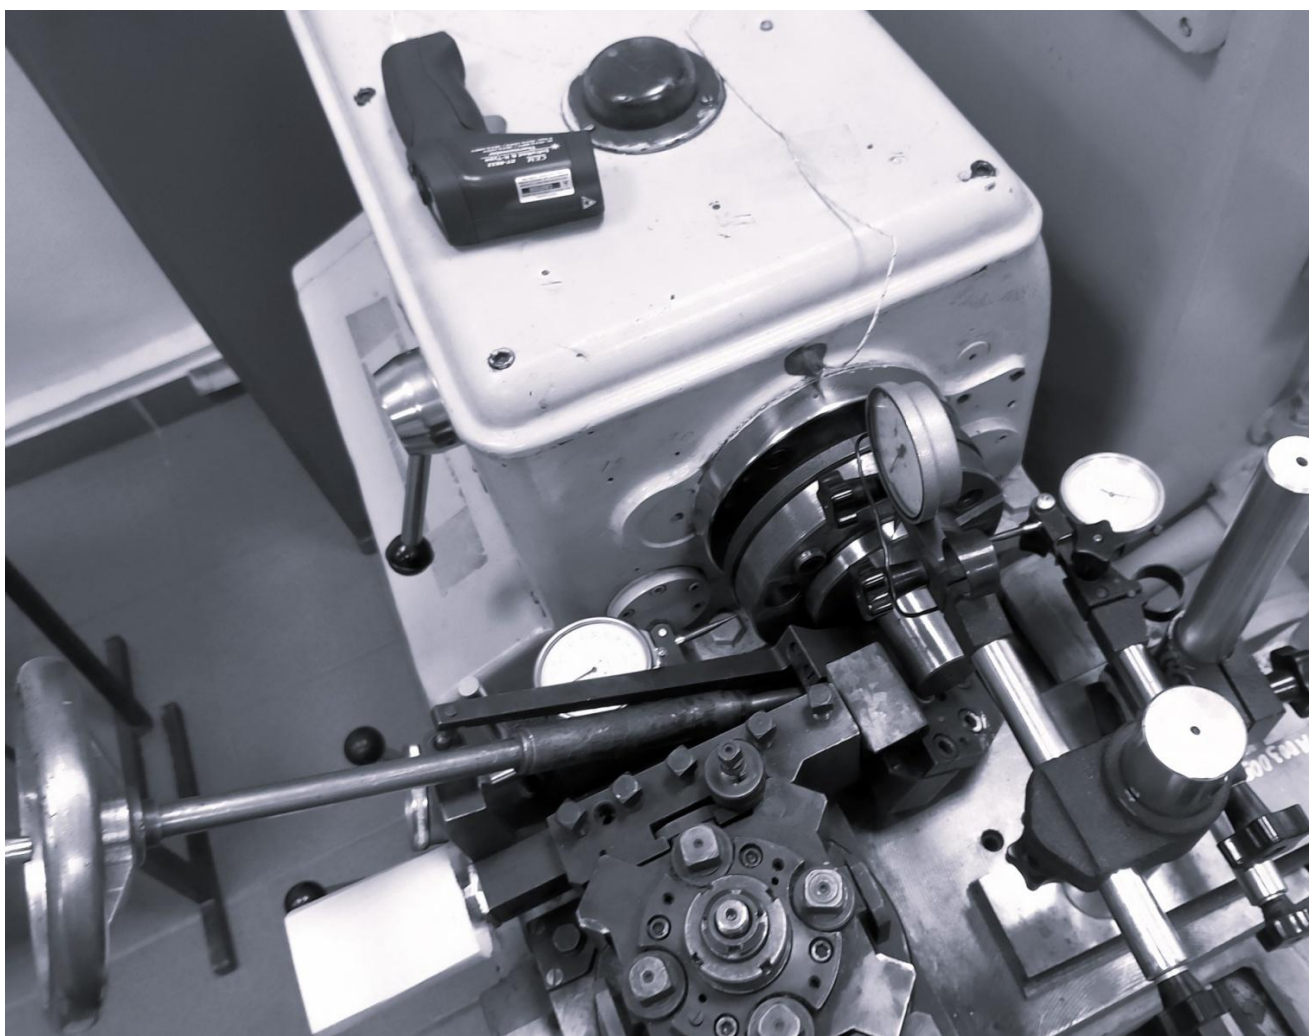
Общий вид экспериментальной установки на базе токарного станка 1А616
